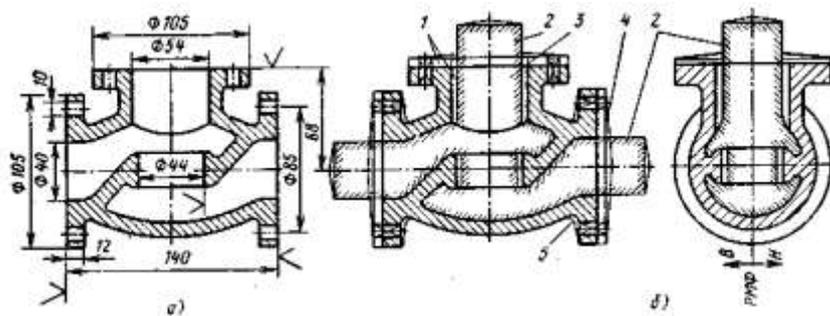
Чертежи детали (а) и литейно-модельных указаний (б) для корпуса вентиля.
